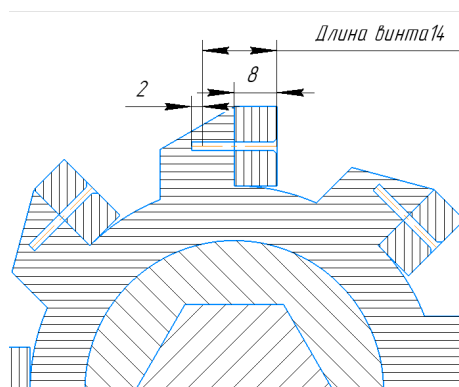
Расчет глубины резьбового отверстия корпуса
